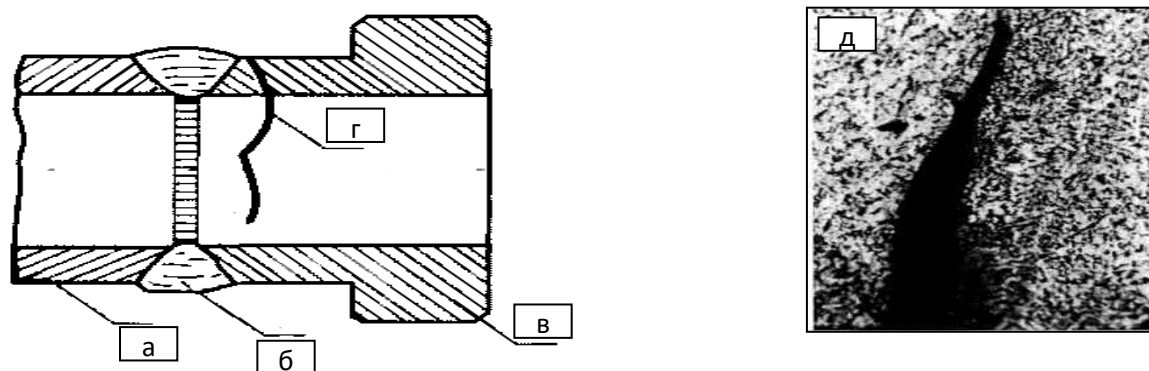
Трещина в сварном шве трубопровода обвязки устья скважины: а) трубопровод б) сварной шов в) фланец г) трещина (слева) д) непровар в корне сварного шва ($\times 300$) (справа)
